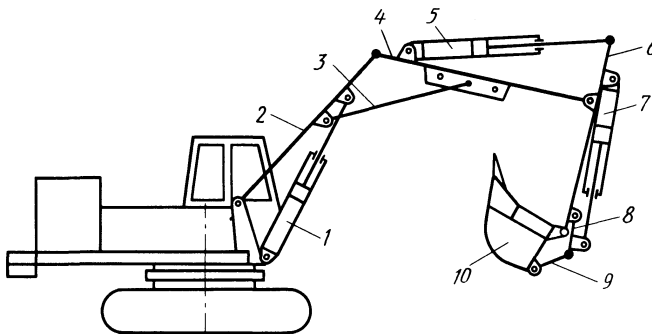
Схема одноковшового гидравлического экскаватора с рабочим оборудованием обратная лопата:
